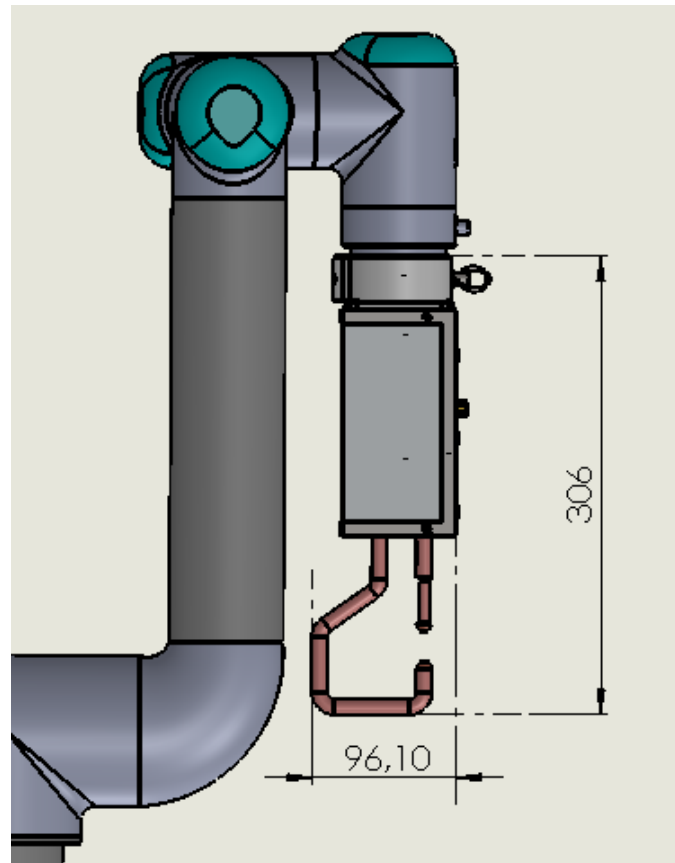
Dimensiones de la pinza de soldadura por puntos acoplada al robot
